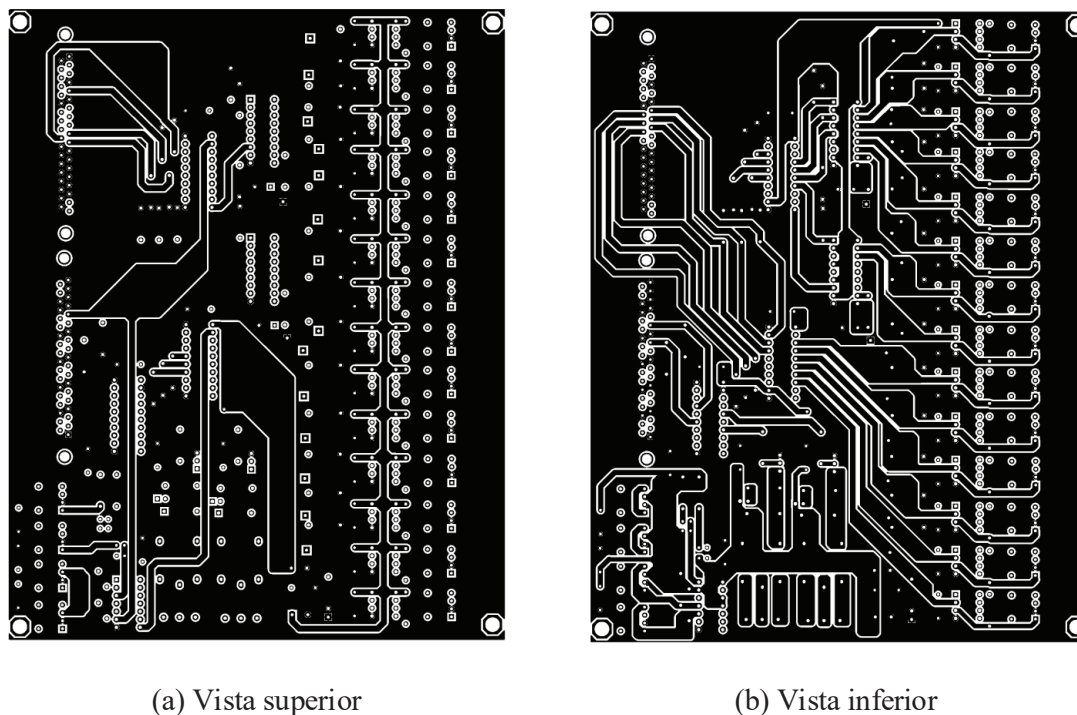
Diseño del PCB de la tarjeta DS1104.
